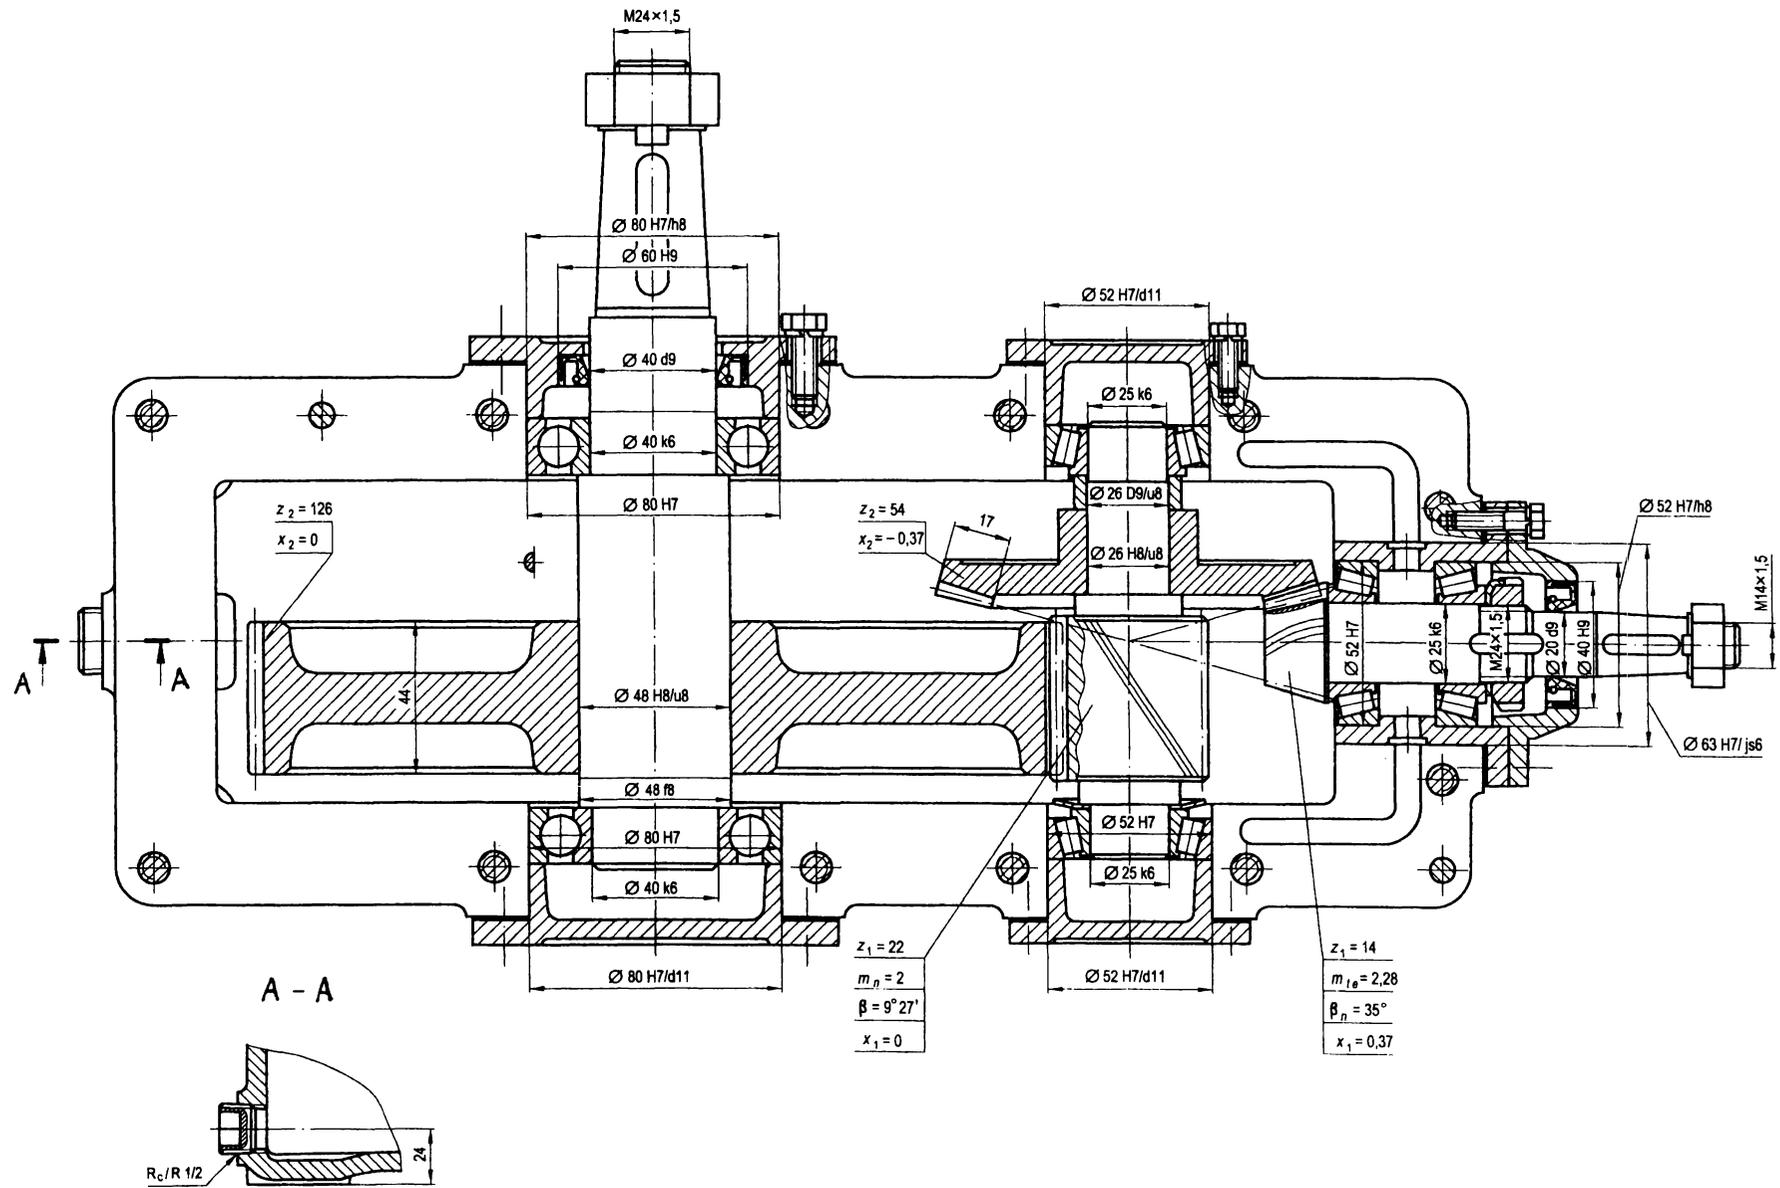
Редуктор коническо – цилиндрический горизонтальный с разъемом корпуса по осям валов
